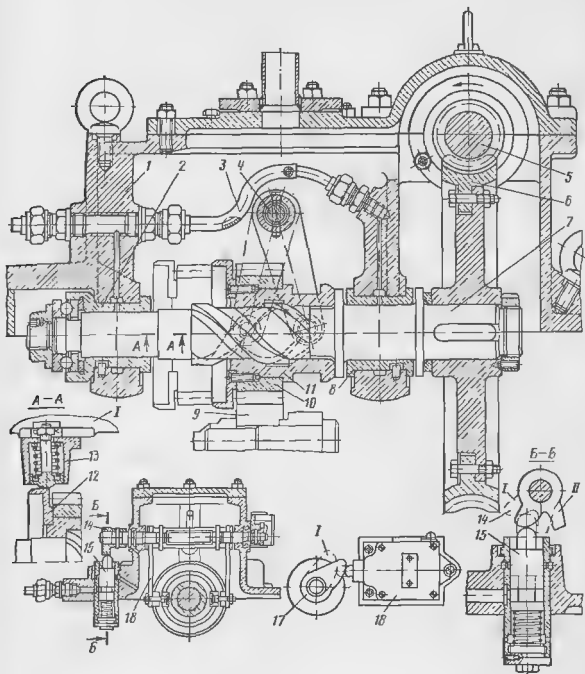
Валоповоротное устройство турбин НЗЛ:
